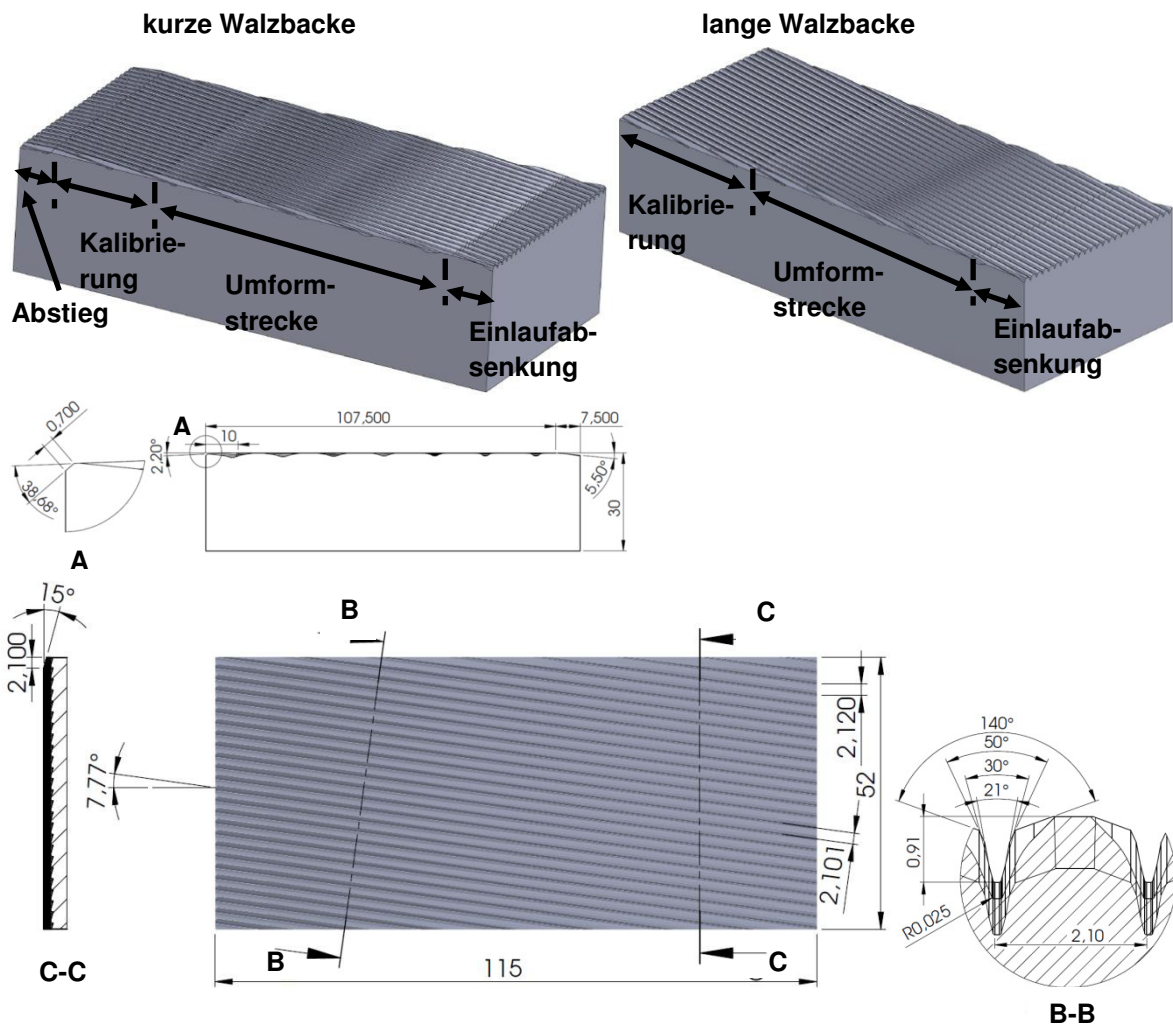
3D-Modelle der Walzwerkzeuge
